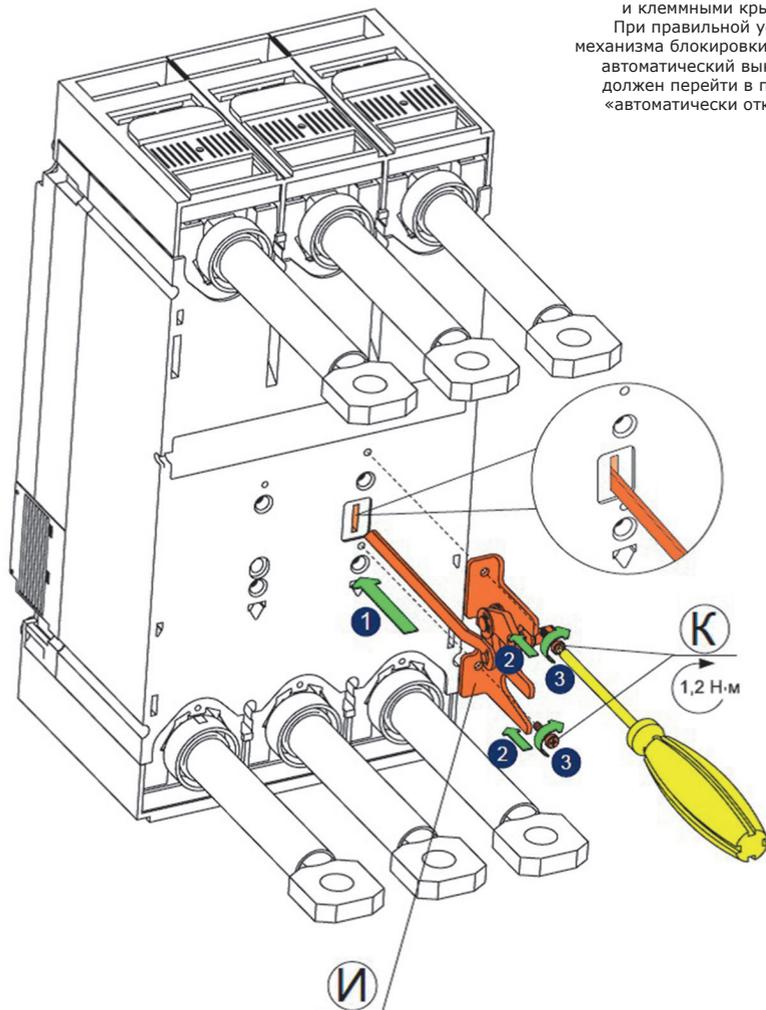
Подготовка стационарного выключателя к установке на раму механической блокировки
